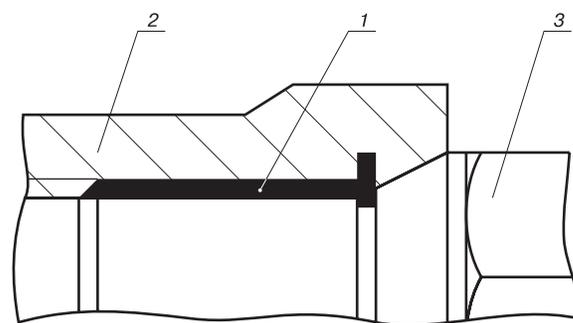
Уплотнение и стопорение резьбового соединения герметиком отверждающегося типа, представляющего собой смесь микрокапсул.
